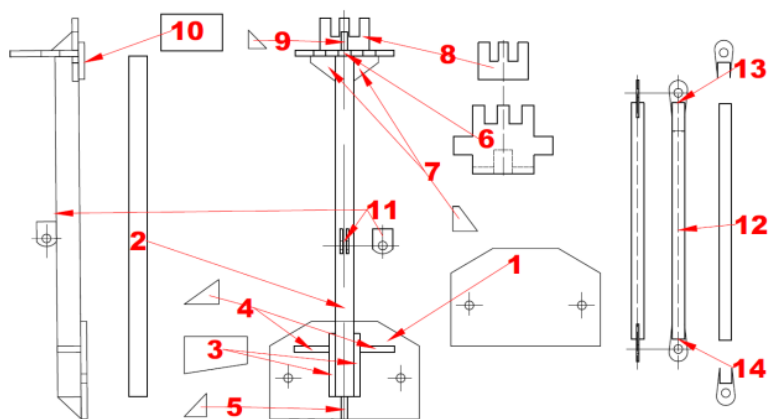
Схема сборки ОКН. Числовые значения от 1 до 14 показывают последовательность установки деталей устройства, для последующей сварки.
